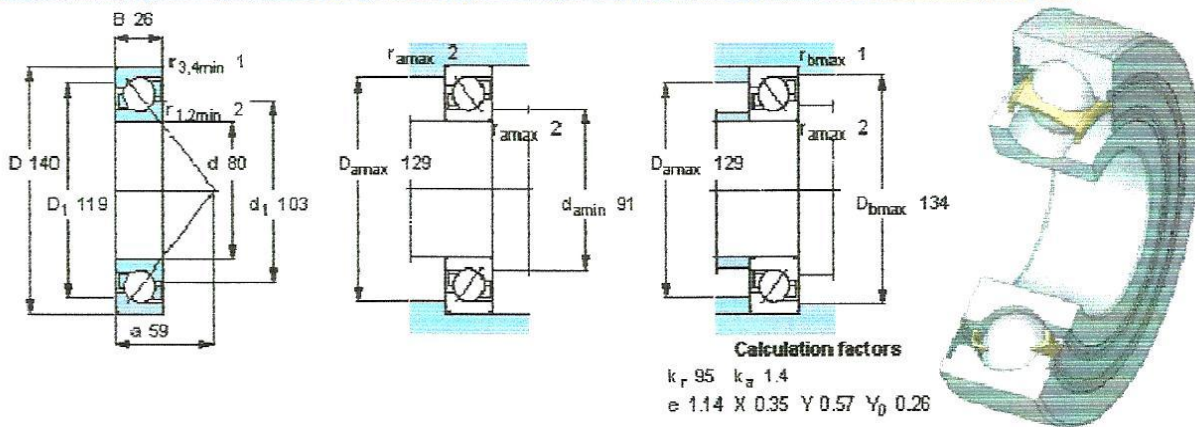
Dimensions du roulement choisi : "7219BEP".
